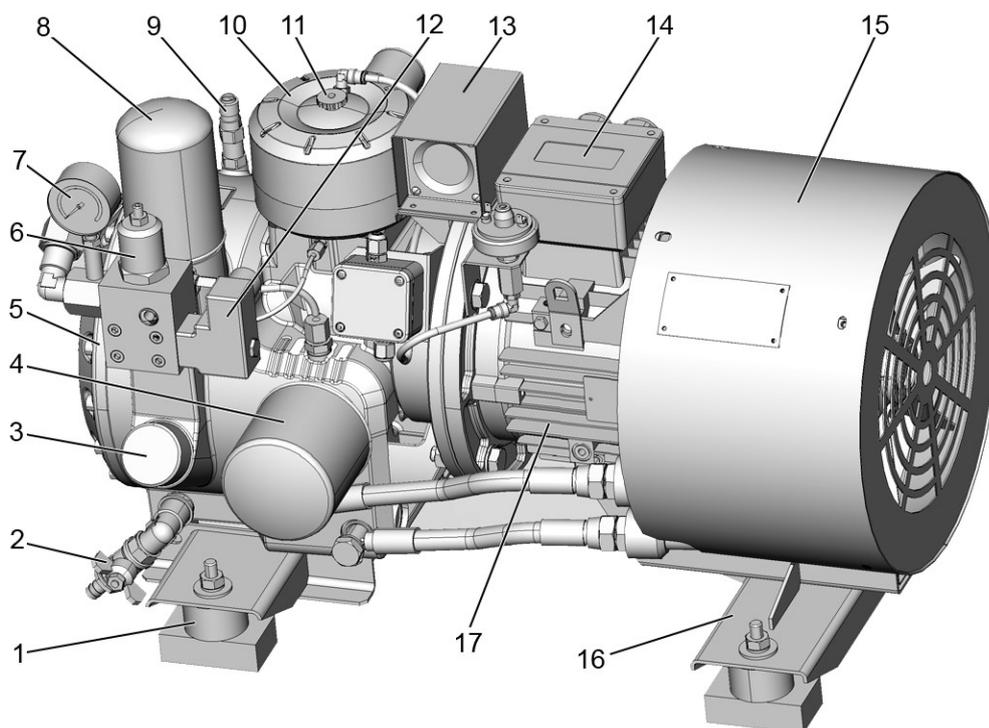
Внешний вид и расположение основных компонентов пневмокомпрессора:
